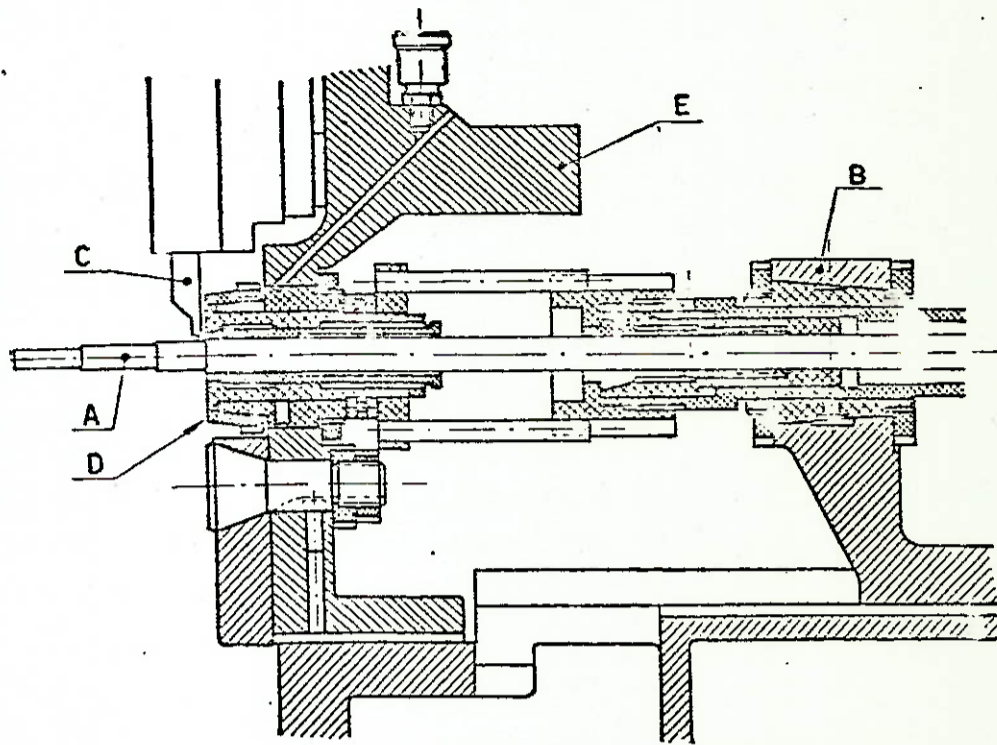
Seção longitudinal do cabeçote do mandril do torno automático «Tornos». (Torneamento com bucha de guia).
